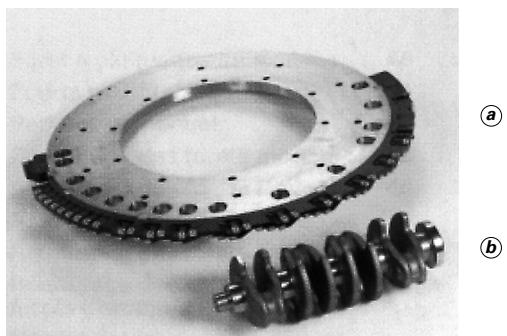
Segment de logement des plaquettes (a) et vilebrequin ainsi que pièce type de fraisage-tournage (b)
